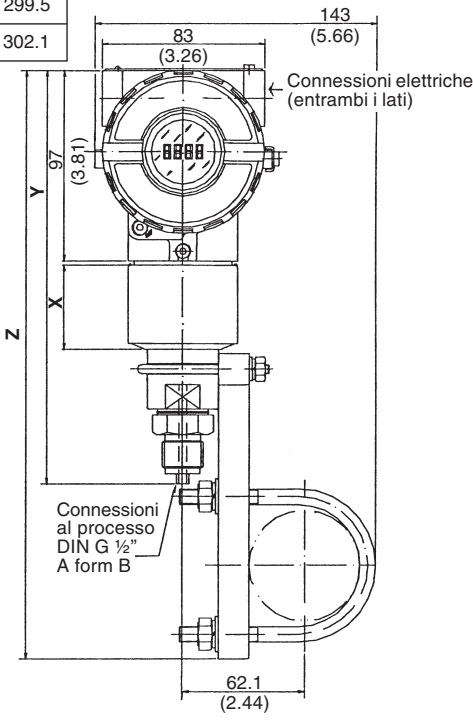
A - Dimensioni di ingombro e posizioni di montaggio per il trasmettitore LD290.
